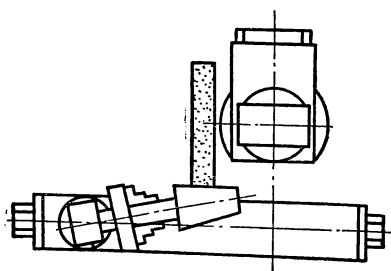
Шлифование конических поверхностей способом поворота передней бабки
